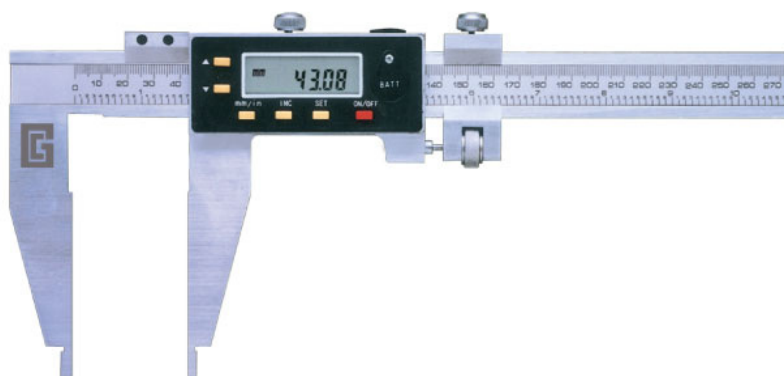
Общий вид штангенциркулей типа ШЦЦ-Ш.
